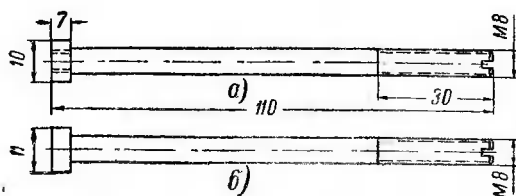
Регулировочный винт упора отключающего механизма привода ПС-10.
